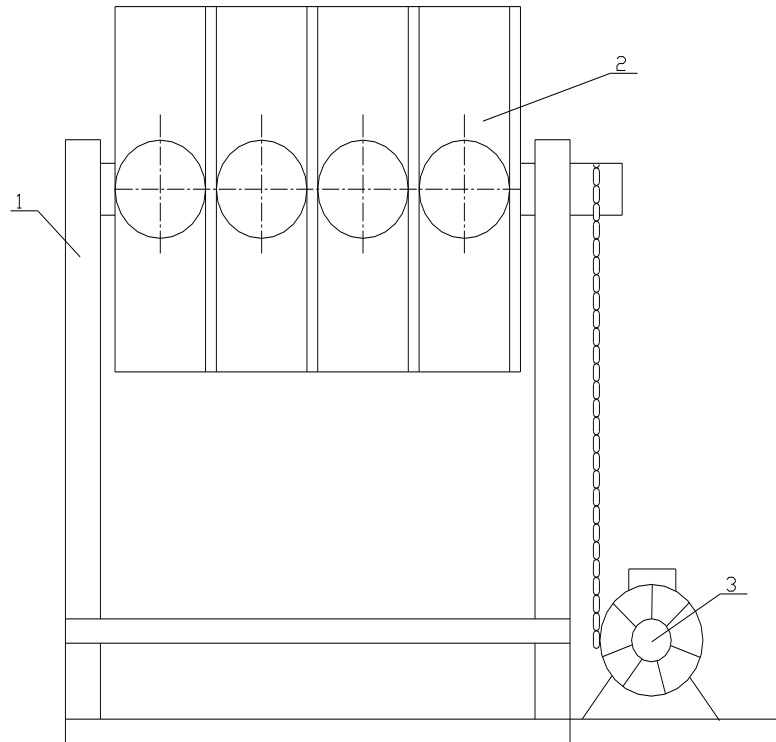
Барабан для випробування коксу. 1 – рама; 2 – барабан; 3 –
